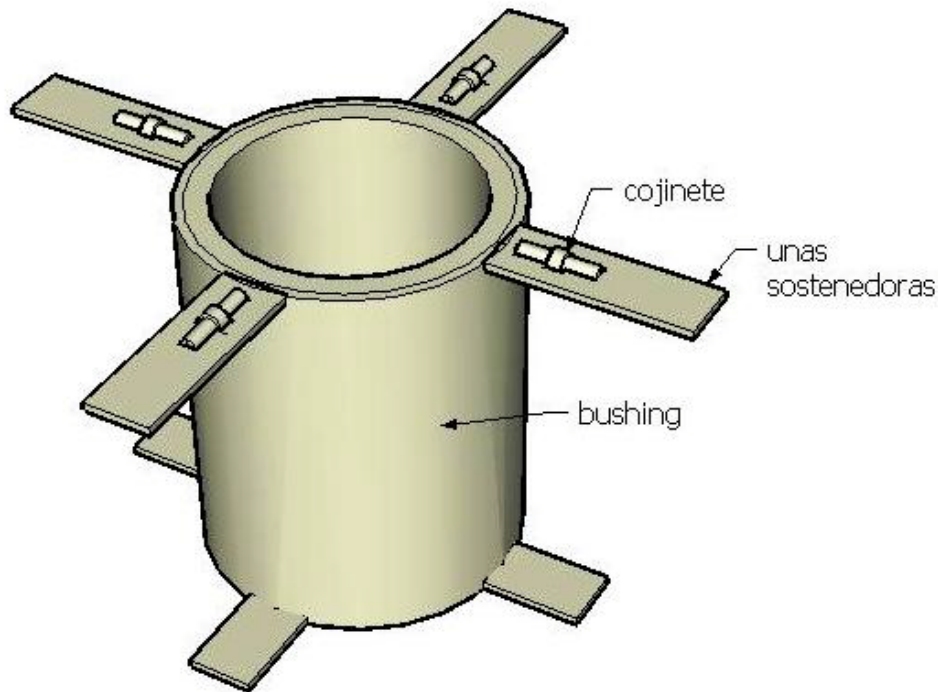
, muestra la forma final que debe tener el bushing antes de ser acoplado a la estructura principal.
